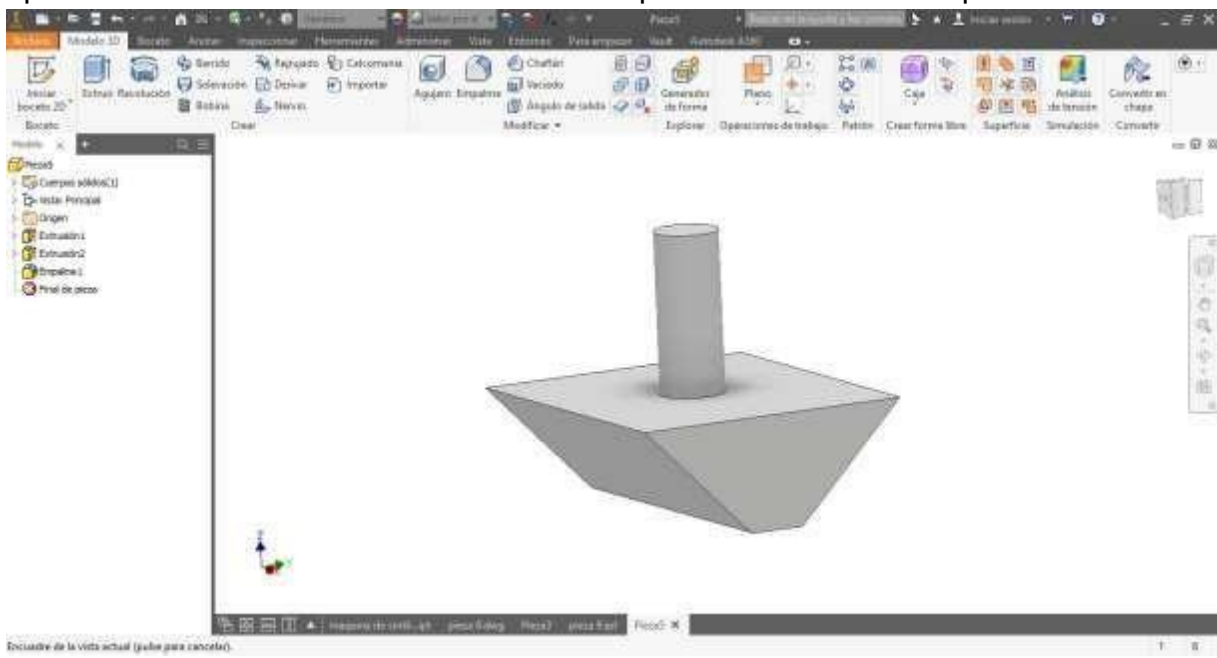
Diseño 3D de molde para troquelado parte superior.
